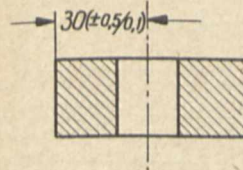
Przykład zwymiarowania płytki pryzmatycznej, uwzględniający cząstkowe tolerancje kształtu.
